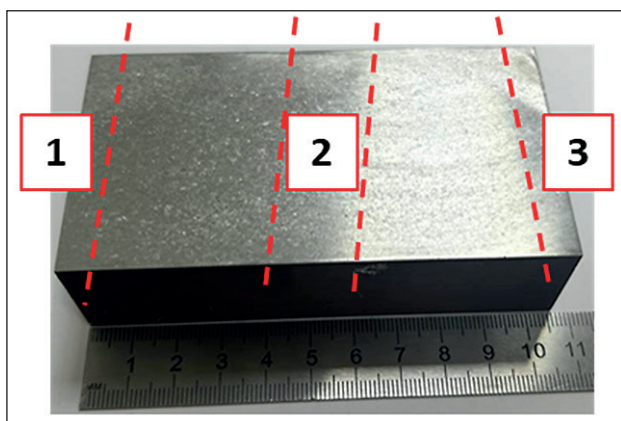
Внешний вид образца из сплава ВТ6 и зоны вырезки на микрошлифы
